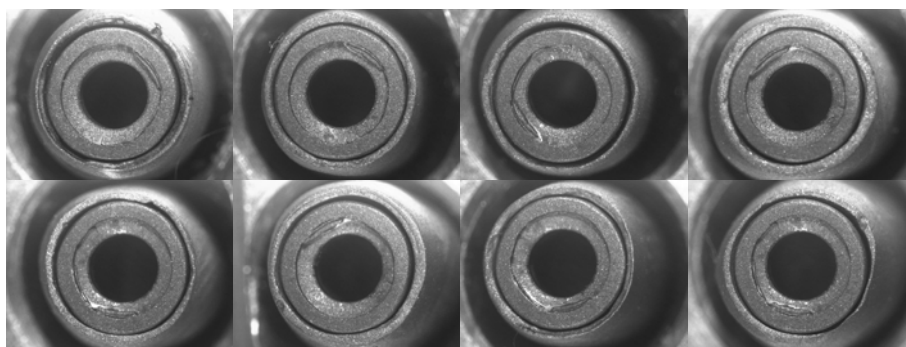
Imagen del complejo pilar de Ti – casquete realizado en pilar de yeso, reubicado.
